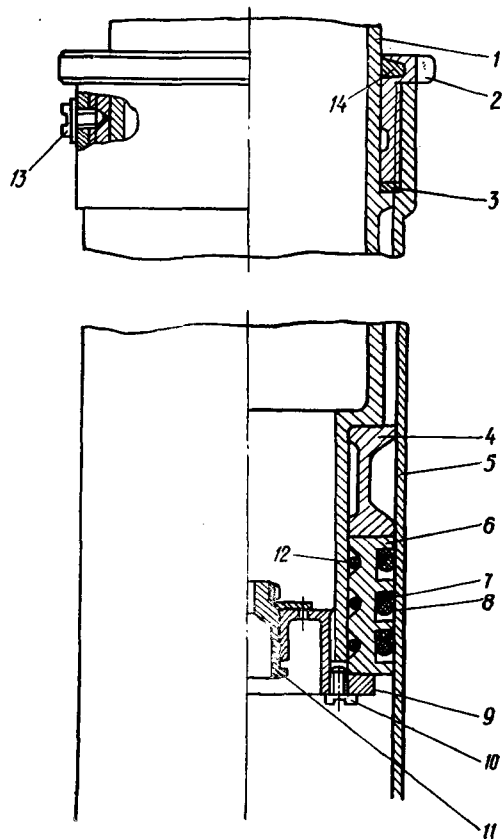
Уплотнение штока амортизатора стойки основной опоры:
